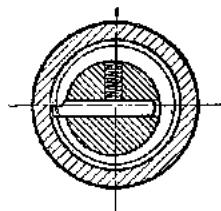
Vista en sección que muestra la herramienta de corte situada a la altura del eje de la pieza que debe roscarse interiormente (South Bend Lathe Works).
